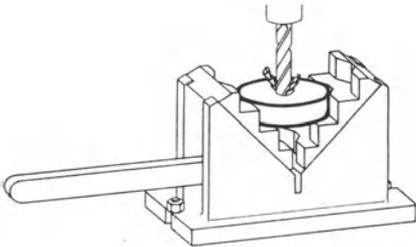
Selbstspannender Zentrierschraubstock für Bohrmaschinen.
